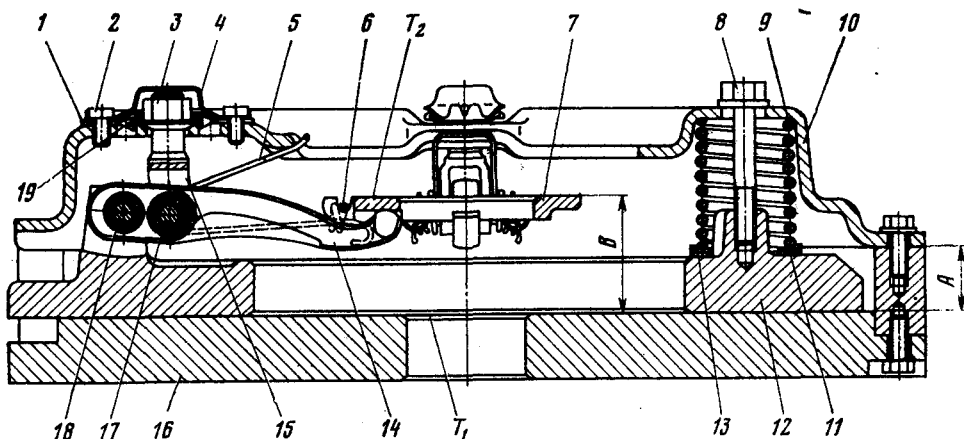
Нажимный диск в сборе с кожухом, установленный на приспособление
